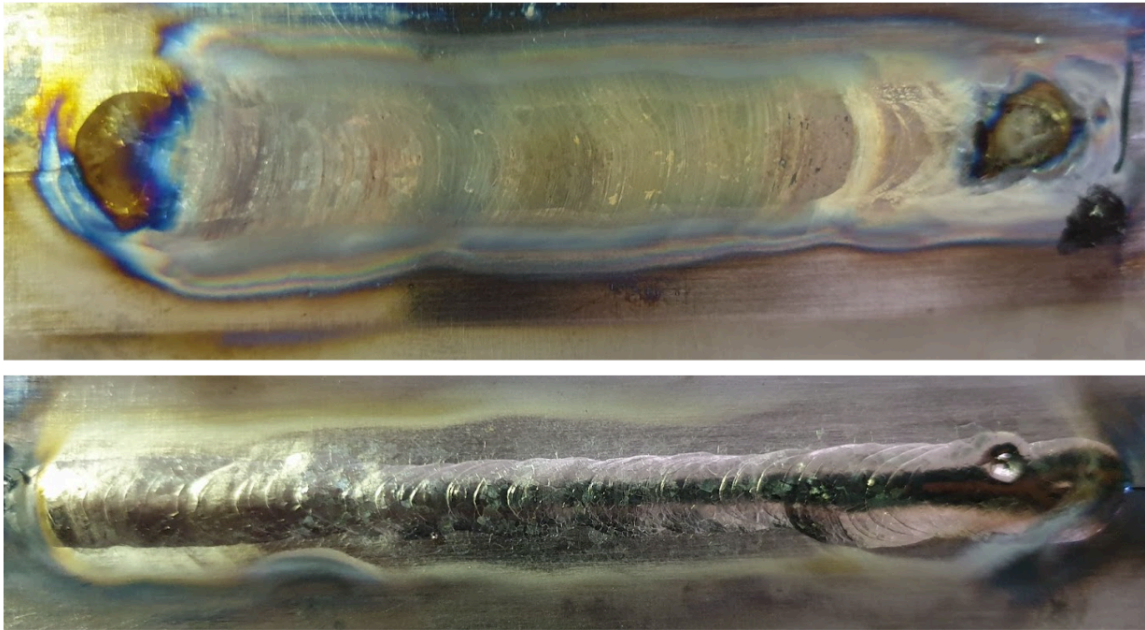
Echantillon O6 (soudure avec un courant continu)
